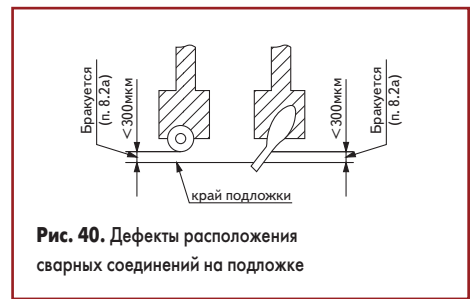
Дефекты расположения сварных соединений на подложке
